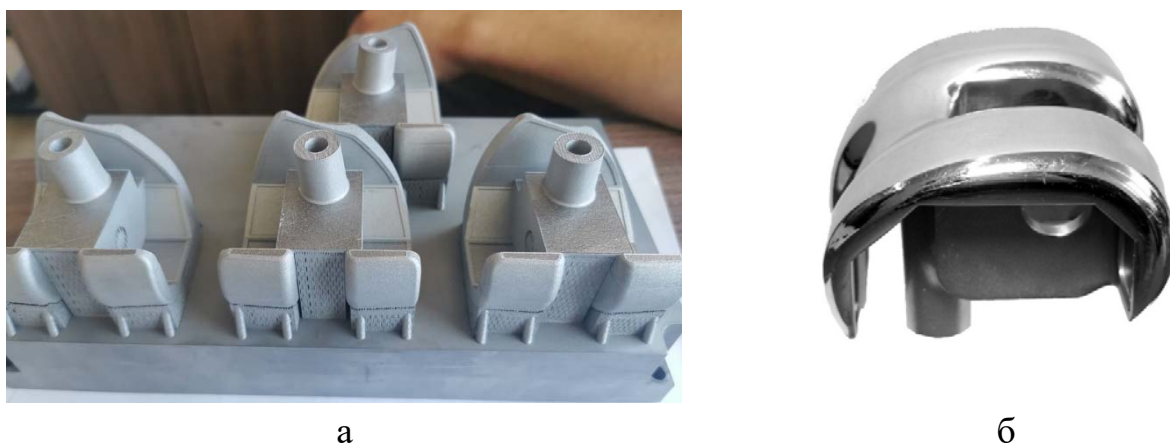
Внешний вид заготовок бедренного компонента эндопротеза коленного сустава после 3D-печати (а), механической обработки и полировки (б)
